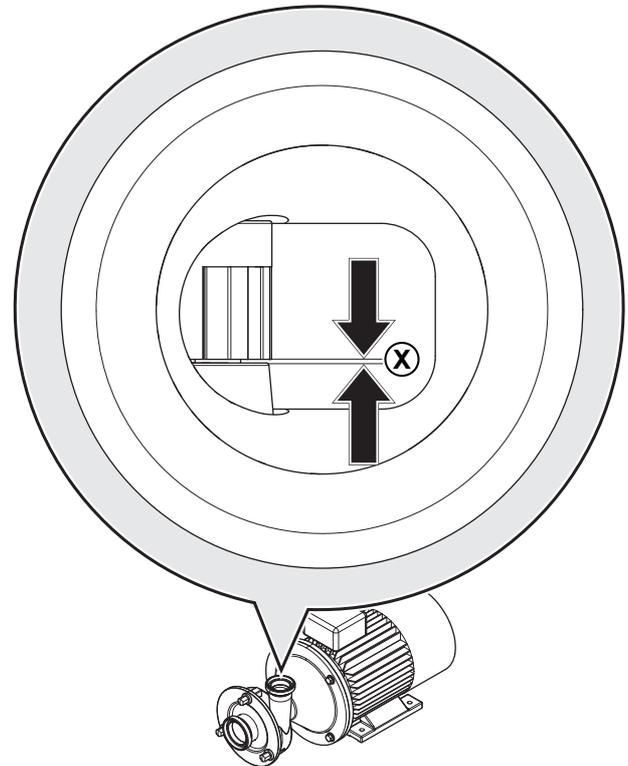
Mesurer le jeu turbine-couvercle de pompe
